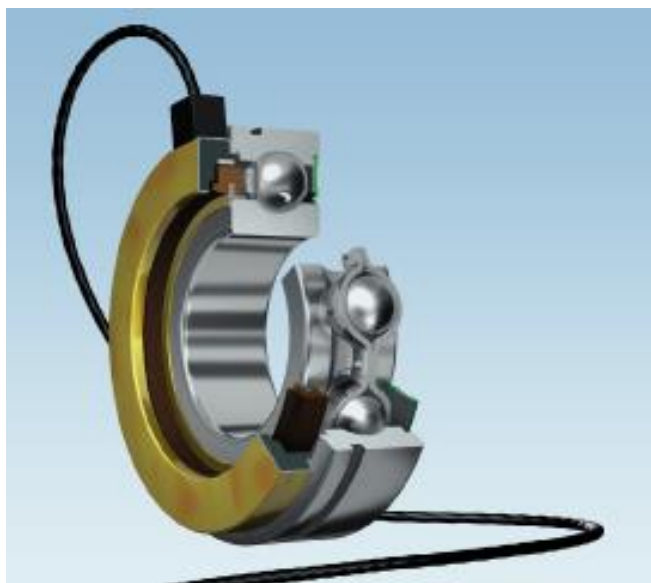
Пример конструкции подшипника со встроенными датчиками
